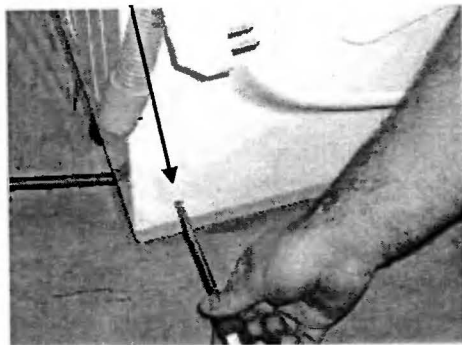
Удаление винтов, крепящих корпус к основанию машины
